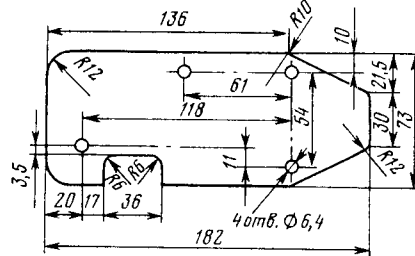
Усилительная пластина крепления механизма ручного привода тормозных механизмов (материал — сталь листовая 08 или 10, толщиной 2—2,5 мм)
